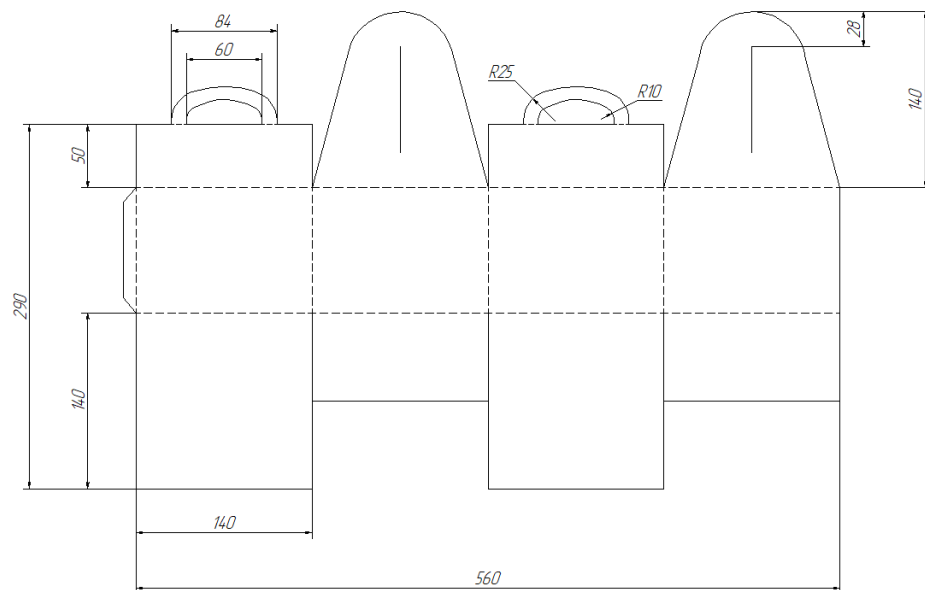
Креслення конструкції пакування для кондитерського виробу
